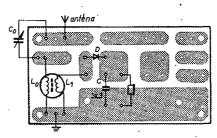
Rozmístění součástek pro krystalku se zesilovačem podle obr. 5c, AR 5/71
